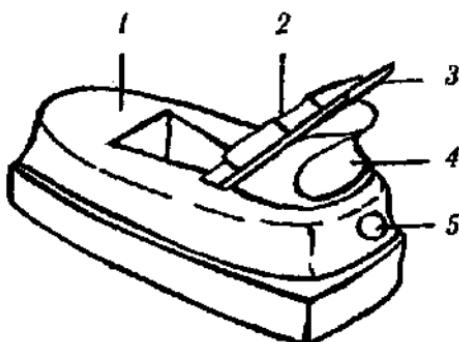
Шлифтик: 1 — колодка; 2 — клин; 3 — двойной нож; 4 — упор; 5 — пробка.
